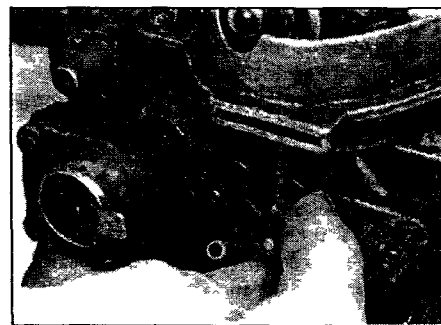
Снимите фиксатор и отсоедините шток вакуумного привода
